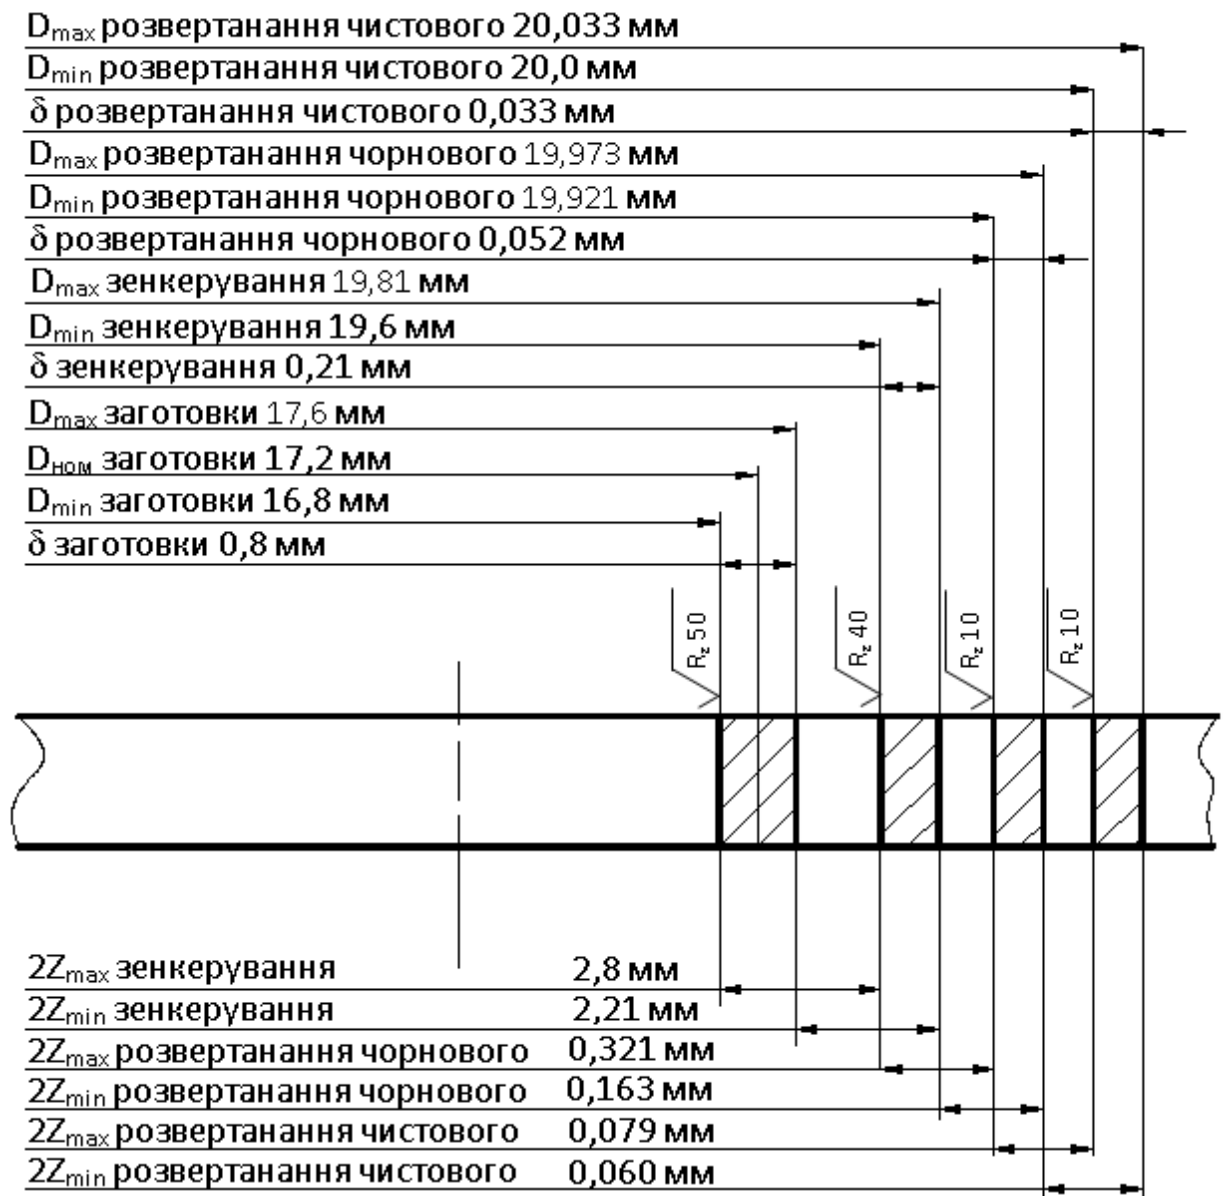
Схема розташування припусків та допусків для поверхні  $\varnothing 20H8$
